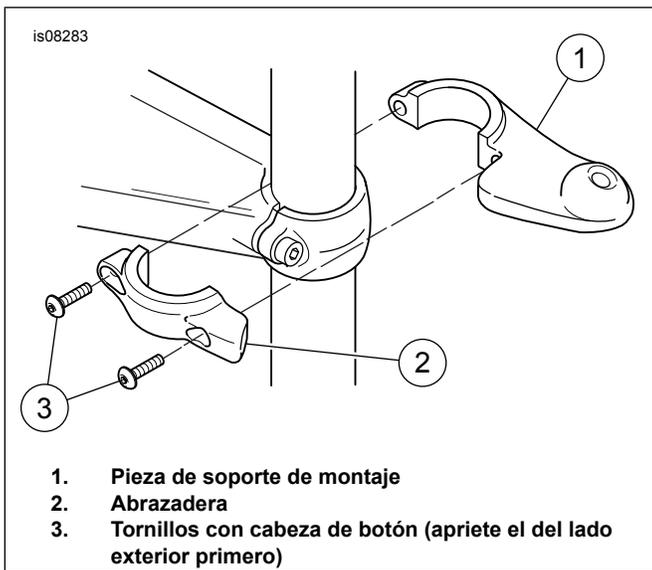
Instalación de la pieza de soporte de montaje en el tubo de la horquilla (se muestra el lado derecho)
